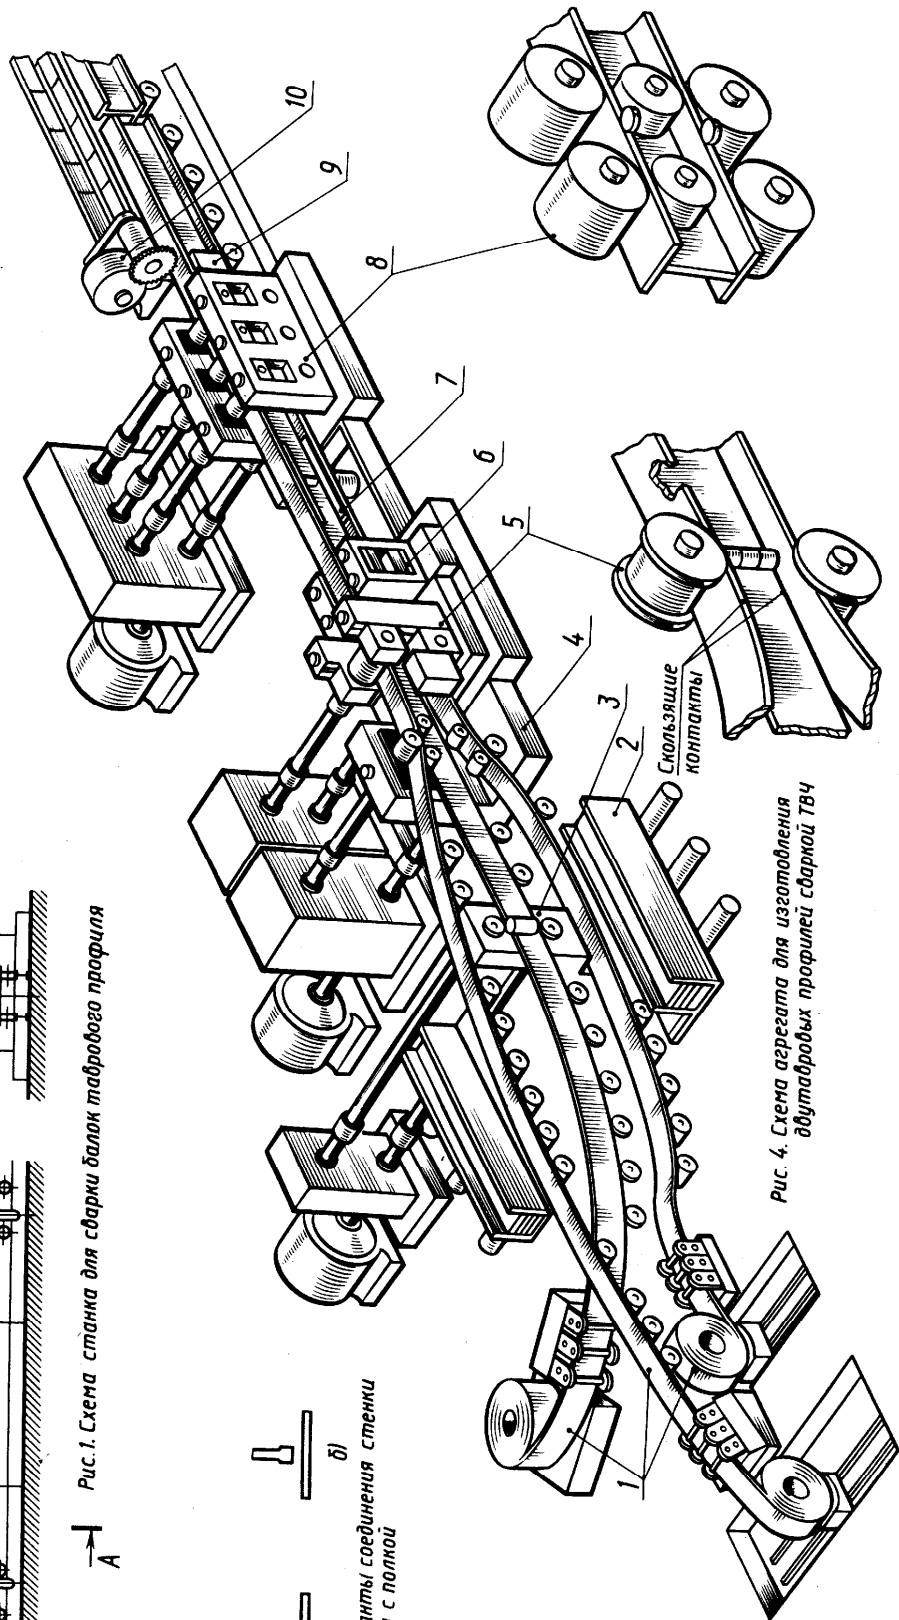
Схема агрегата для изготовления двутавровых профилей сваркой ТВЧ
